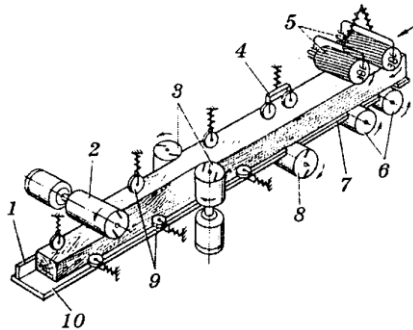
Принципова схема чотирибічного поздовжньо-фрезуального верстата: 1 — напрямна лінійка; 2 — верхня горизонтальна ножова головка; 3 — права і ліва вертикальні ножові головки; 4 — притискні ролики; 5 — рифлені вальці; 6 — гладкі вальці; 7 — передній стіл; 8 — фугувальна ножова головка; 9 — підпружинені ролики; 10 — задній стіл
